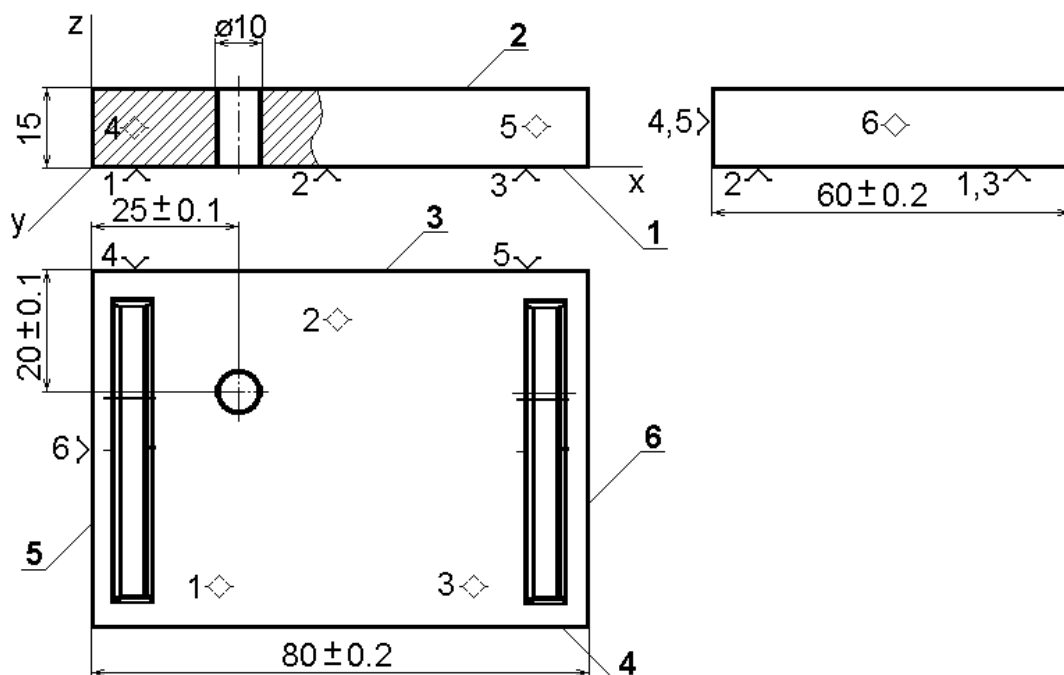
Выбор базовых поверхностей и теоретическая схема базирования детали
